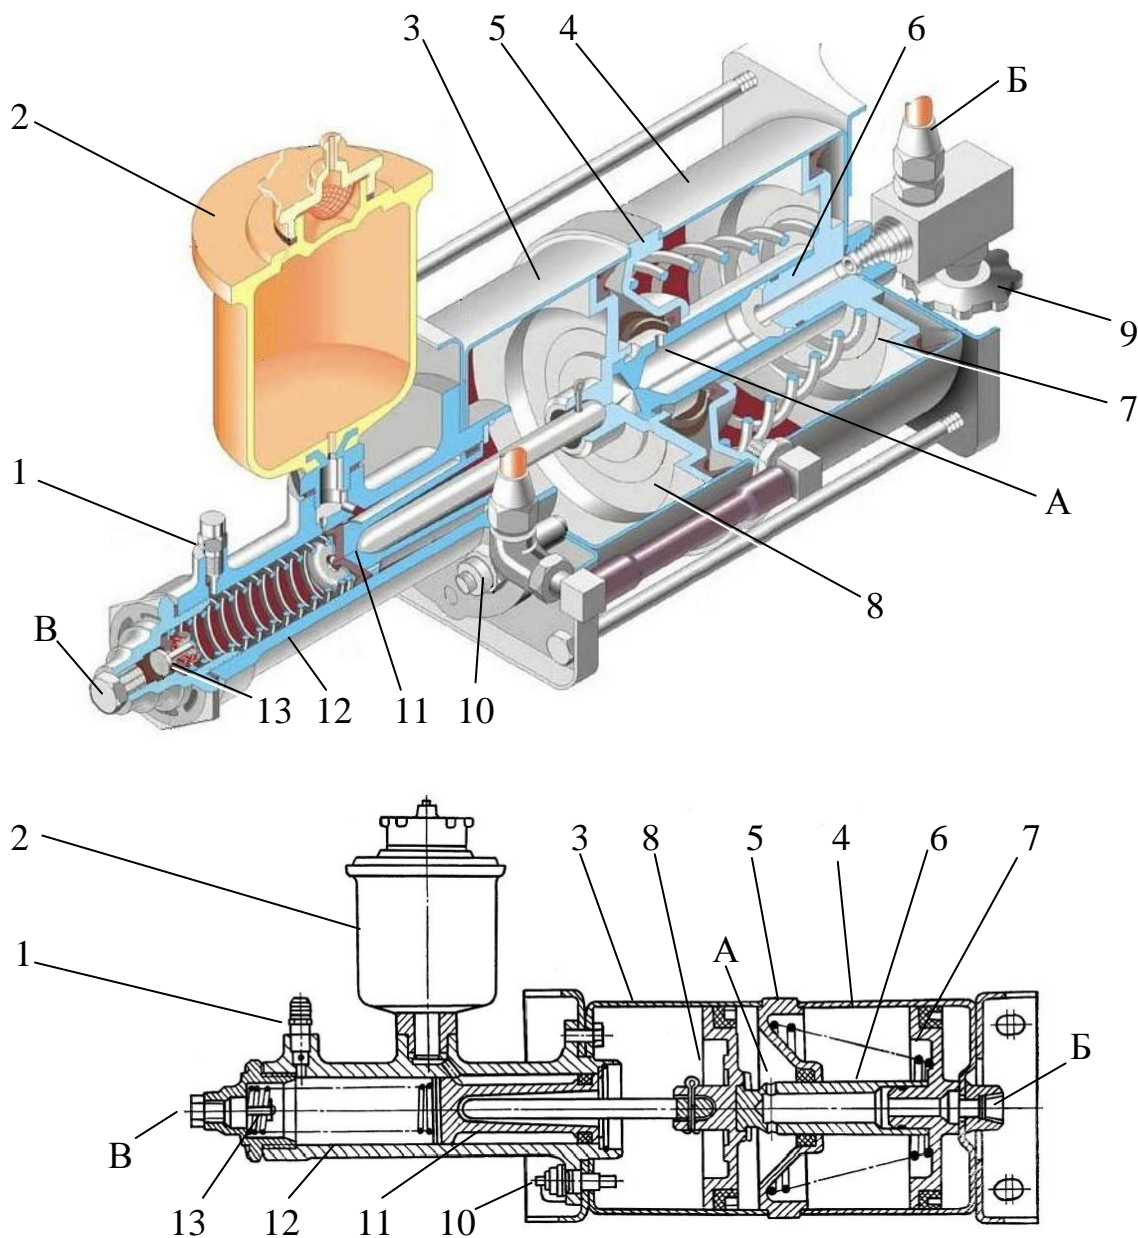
Конструкция пневмогидравлического аппарата с главным тормозным цилиндром: 1 – клапан выпуска воздуха из гидропривода; 2 – бачок для тормозной жидкости; 3, 4 – пневмоцилиндры; 5 – проставка; 6 – шток; 7, 8 – поршни пневмоцилиндров; 9 – клапан контрольного вывода; 10 – включатель сигнализатора неисправности тормозов; 11 – поршень главного тормозного цилиндра; 12 – главный тормозной цилиндр; 13 – обратный клапан; А – радиальное отверстие; Б – вход из пневмосистемы от тормозного крана; В – выход к колесным гидроцилиндрам (на рисунке показан закрытым заглушкой)
